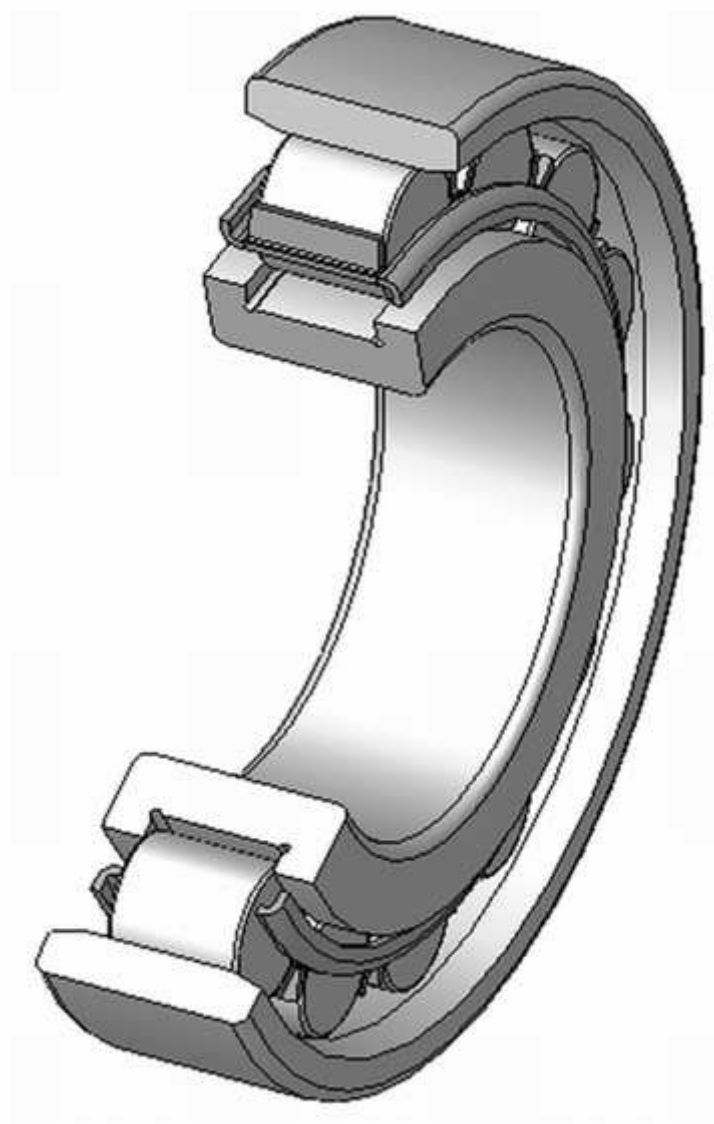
Роликовый радиальный подшипник с короткими цилиндрическими роликами
